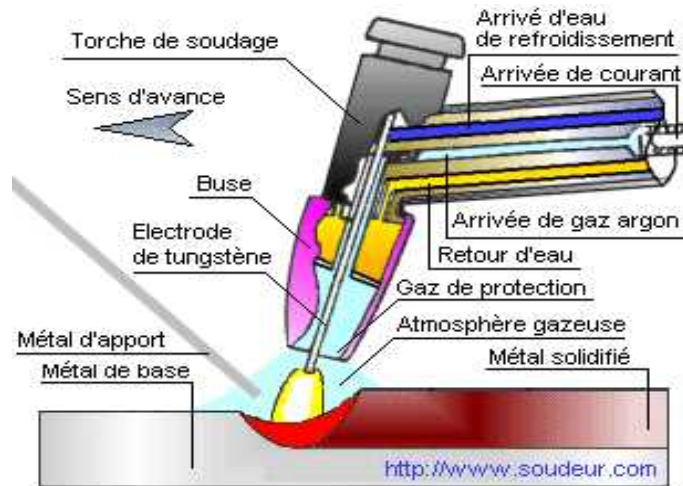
Procédé de soudage TIG (avec sa torche) [Daigle 2003a].
